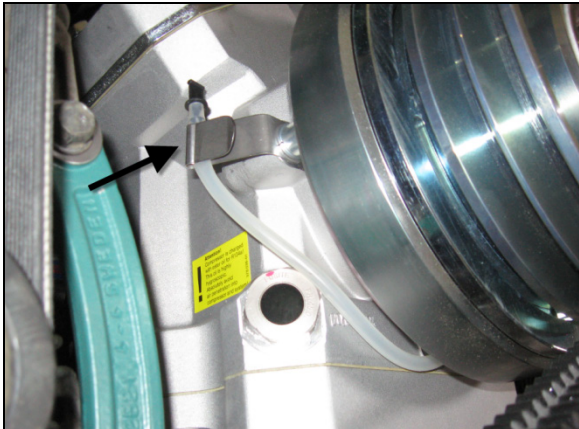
TUBE COLLECTEUR D'HUILE DU JOINT D'ARBRE
